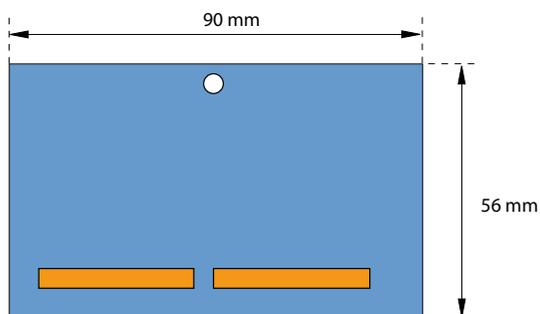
Dimensioni del modulo di sistema (struttura D)
